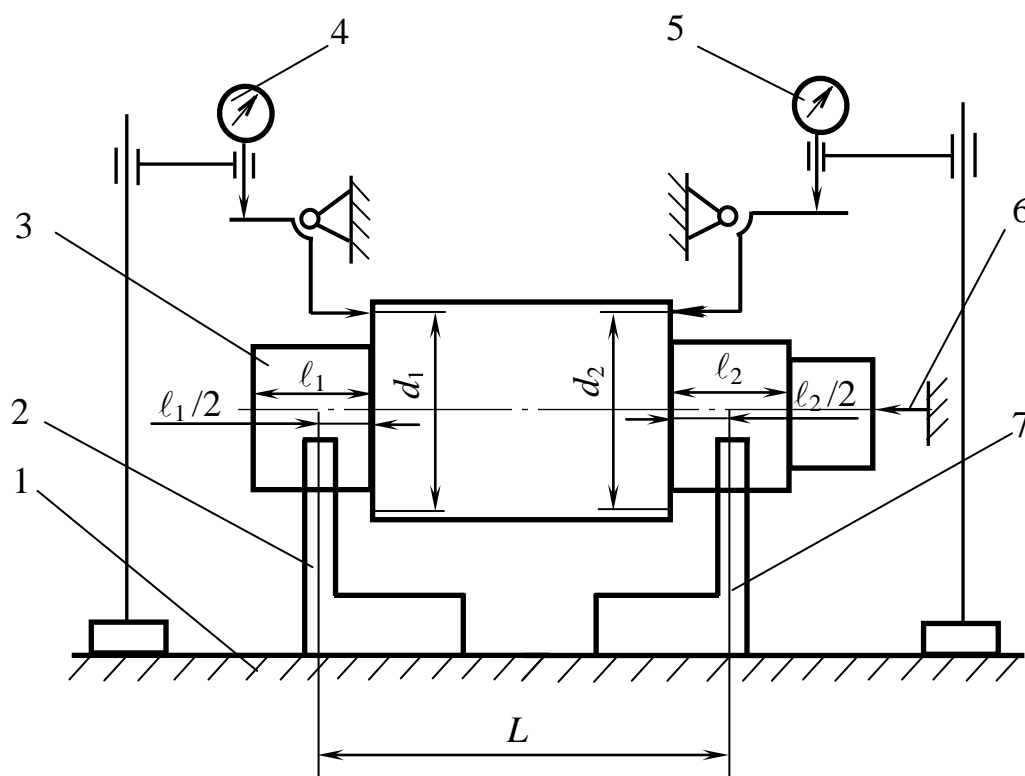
Схема измерения торцового биения заплечиков вала относительно общей оси шеек под подшипники: 1 – поверочная плита; 2 и 7 – ножевидные призмы; 3 – измеряемая деталь; 4 и 5 – индикаторы часового типа; 6 – упор
